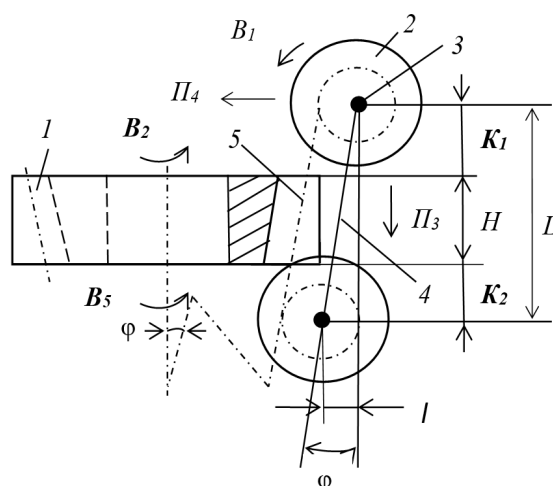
Способ фрезерования цилиндрических зубчатых колес с наклонными зубьями
